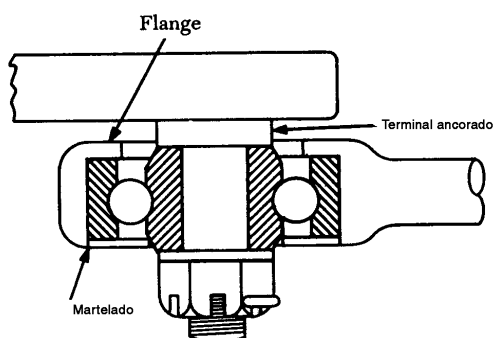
5 Flange da haste interposto entre a pista do rolamento e o terminal do parafuso.
